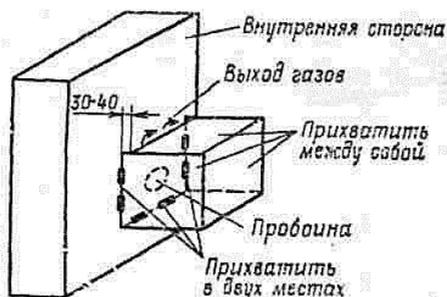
Пример установки защитного кармана из тонколистовой стали
